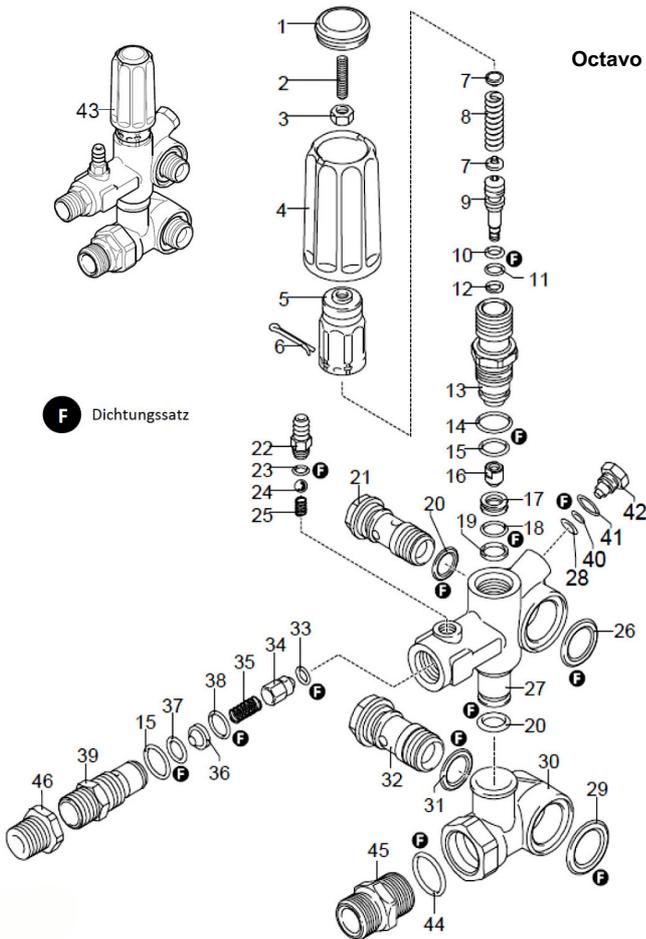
Plano de repuestos 7 y plano de repuestos 8 HDR-K 96-28 BL
